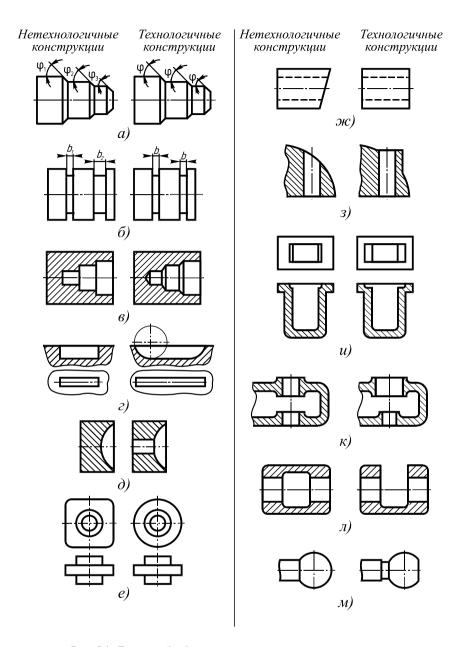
Детали, обрабатываемые на металлорежущих станках
